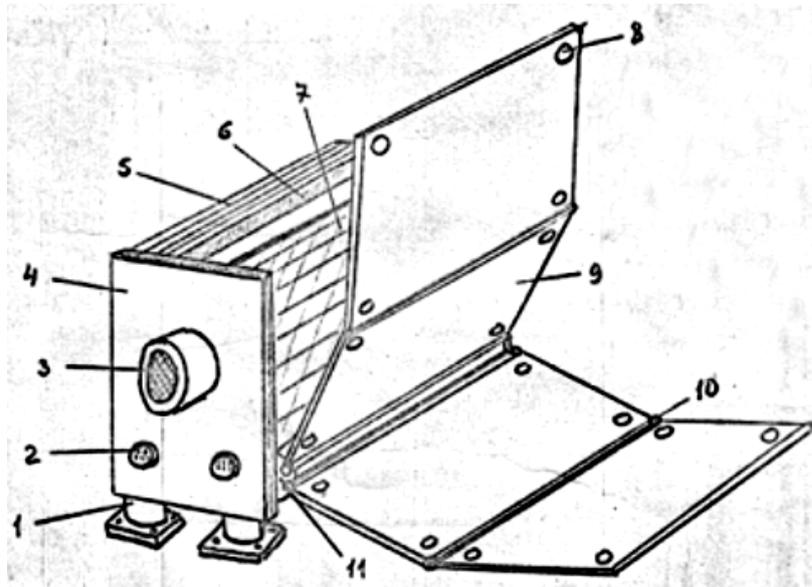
Книжная компоновка блока МЭА с горизонтальной осью раскрытия: 1 - амортизатор; 2 - разъем; 3 - воздуходувка; 4 - передняя панель; 5 - пакет ФЯ; 6 - средняя стенка; 7 - гибкий шлейф; 8 - отверстие для стяжки; 9 - ФЯ; 10 - межъячеечный шарнир; 11 - общий
